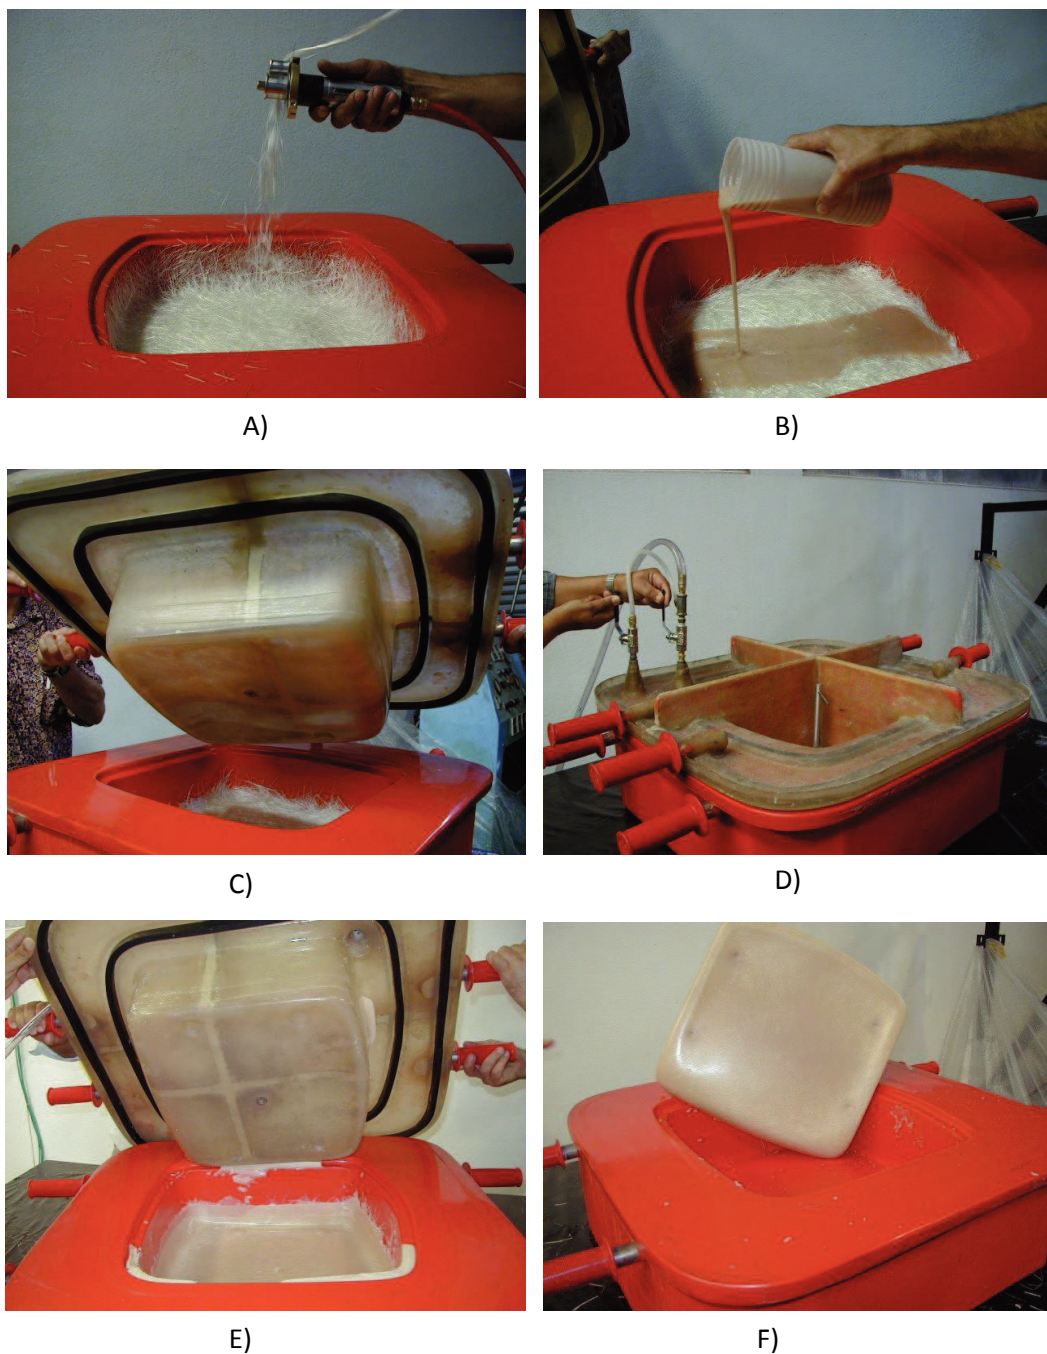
Processo de moldação por Vácuo. A) Deposição do roving B) Deposição manual da resina C) Fecho do molde D) O vácuo é acionado para fechar o molde E) Peça antes de ser desmoldada e a resina no canal de excesso F) Peça final com 2 faces lisas. (owenscorning, s.d.)
